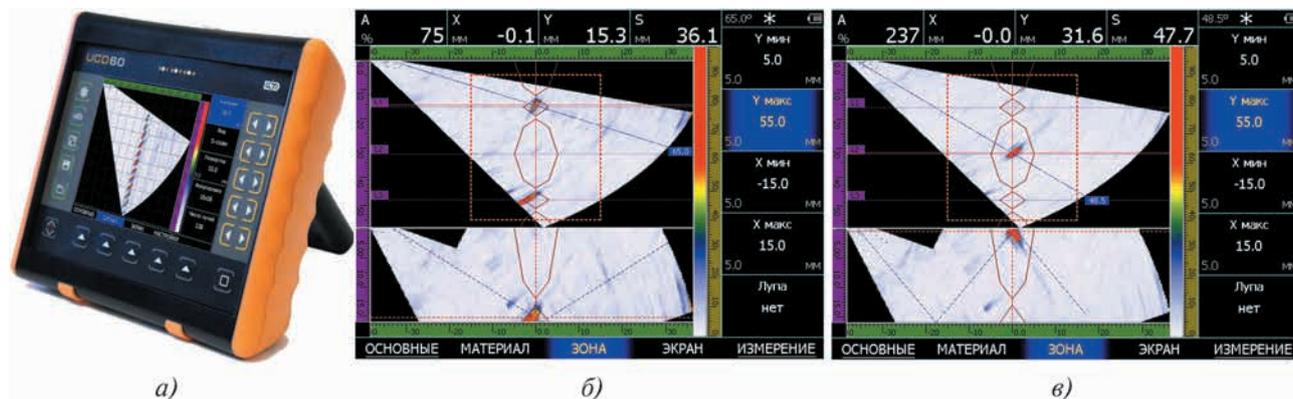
Дефектоскоп УСД-60 ФР (а), наглядное изображение сварного соединения с дефектом в корне сварного соединения (б) и в верхней части шва (в)
